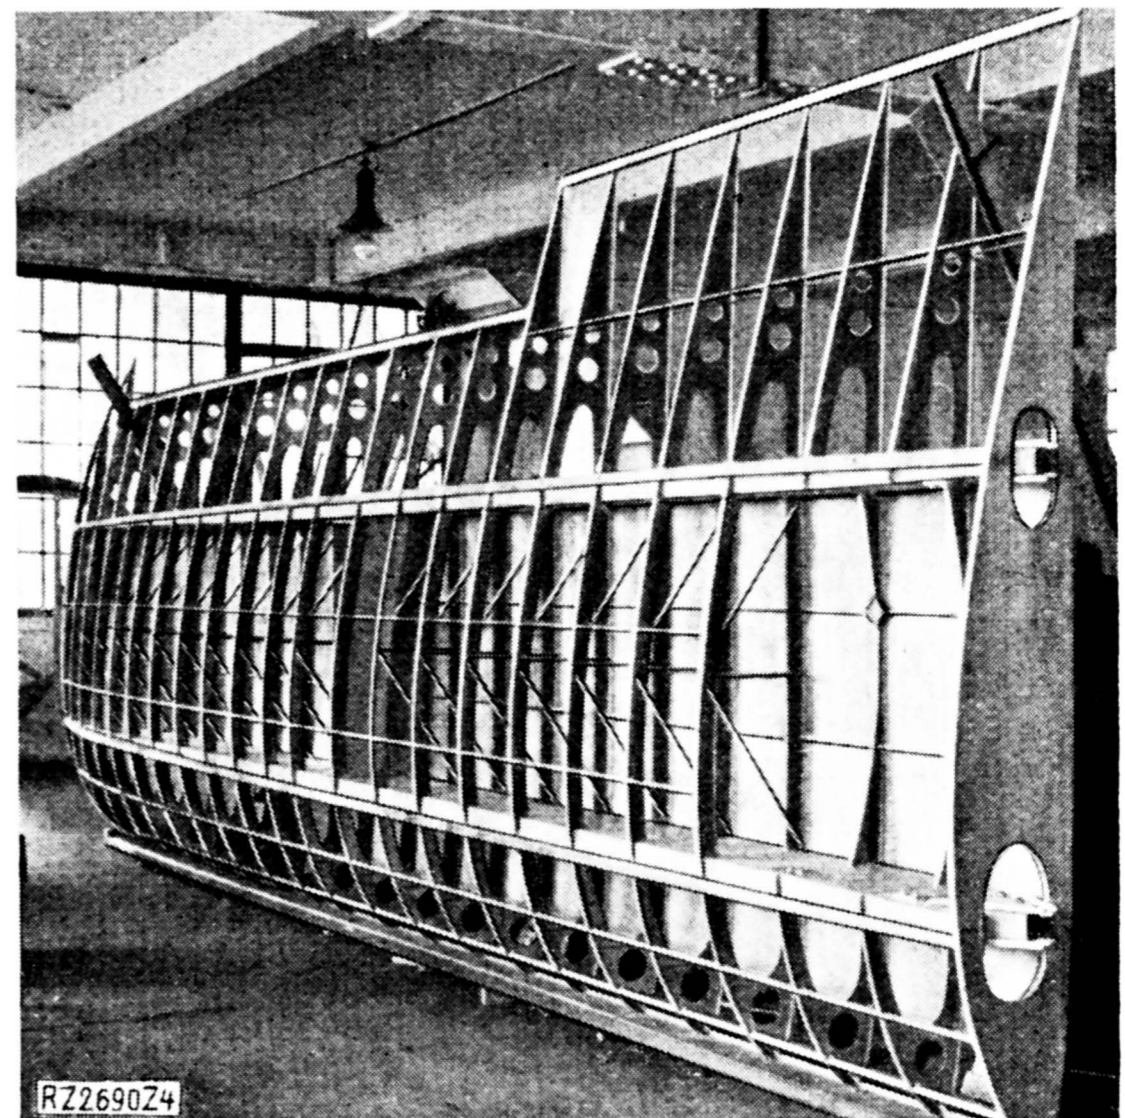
Flächengerippe aus Holz des Flugzeuges, Abb. 3.
